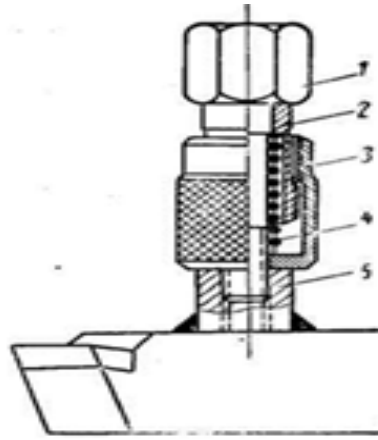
Гаситель ударного действия: 1 – сердечник; 2 – втулка; 3 – крышка; 4 – разжимающая пружина; 5 – переходная гайка
